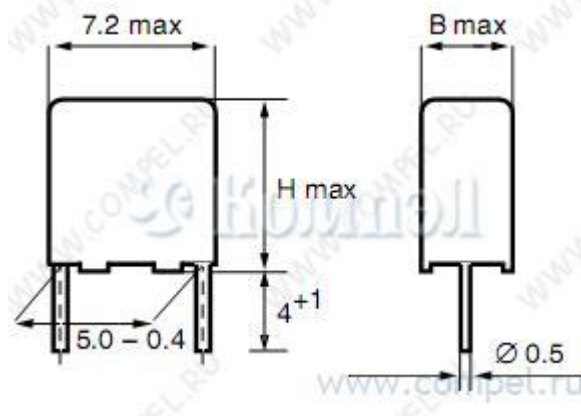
Габаритні розміри В32529С1102J000 "Epcos"
